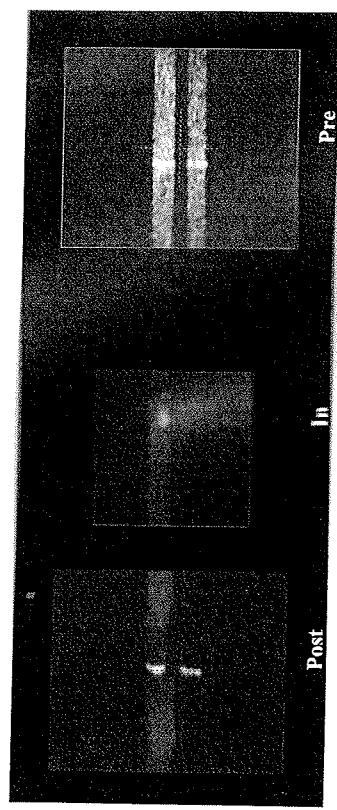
Realbauteil Bosch (Messung S049, Bild-Nr. 89, mit Spalt).
